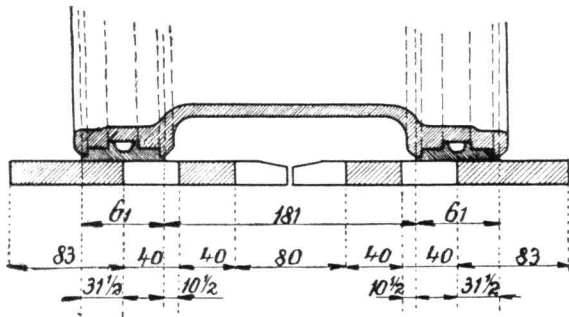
Dimensionierung der für die Steuerung wichtigen Kanten des Schieberspiegels und des Hochdruckkolbenschiebers.
